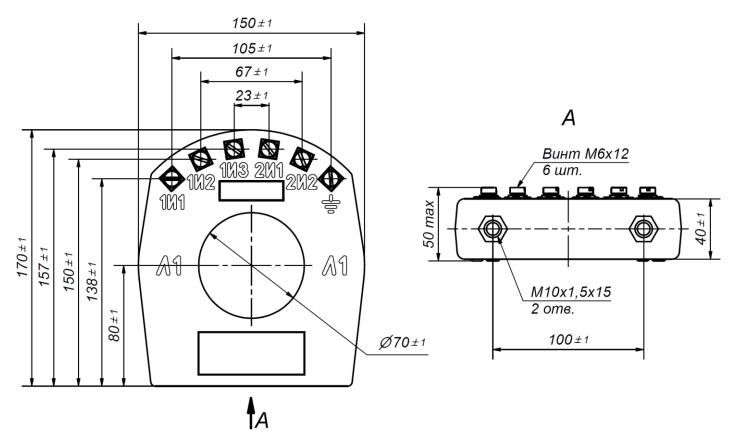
Габаритный чертеж трансформатора тока ТЗЛУ-70.
